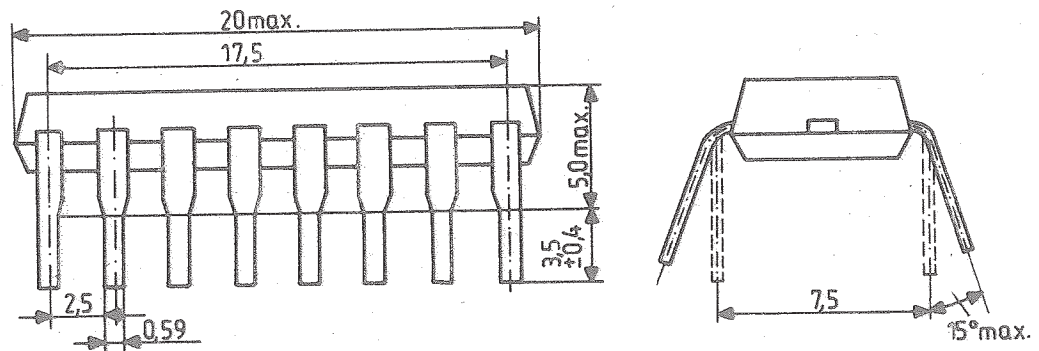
Gehäuseabmessungen des KR 537 RU 1
